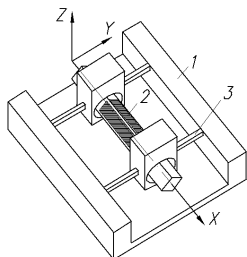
Макет пьезогироскопа: 1 – корпус; 2 – балочный чувствительный элемент; 3 – подвеска
